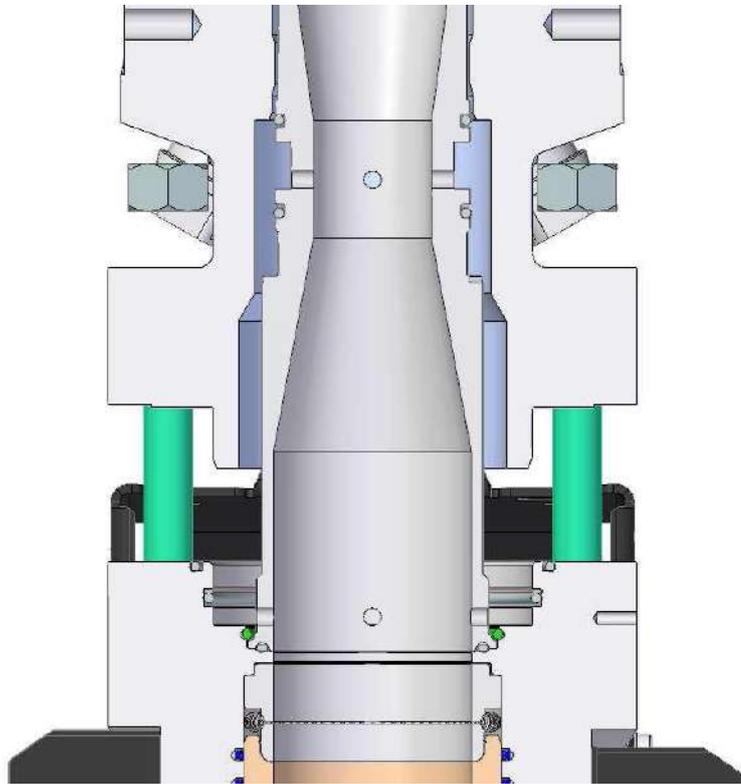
Подъем корпуса/верхнего фланца трубки Вентури с корпуса расходомера
